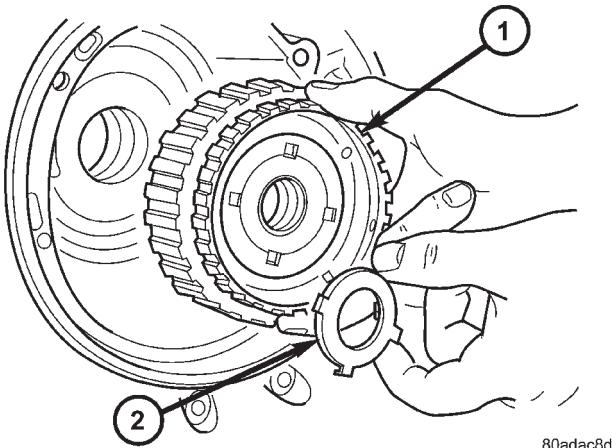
Instalación del conjunto del portador delantero y el engranaje anular trasero
